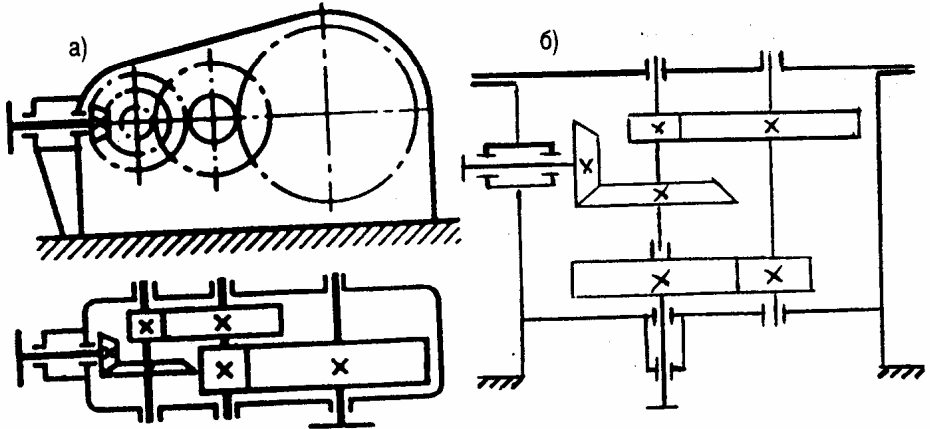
Кинематические схемы коническо-цилиндрических трехступенчатых редукторов (КЦ2)
